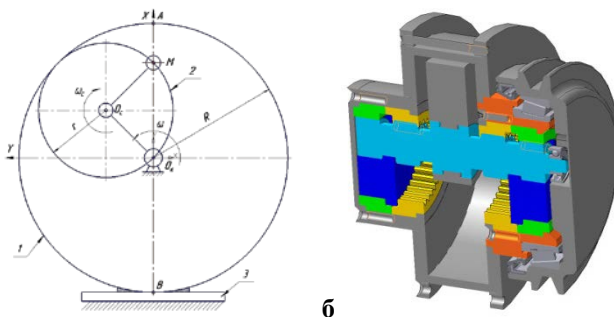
Схема планетарного механизма с соотношением диаметров колёс  $D:d = R:r = 2:1$  (а), модель механизма (б)
